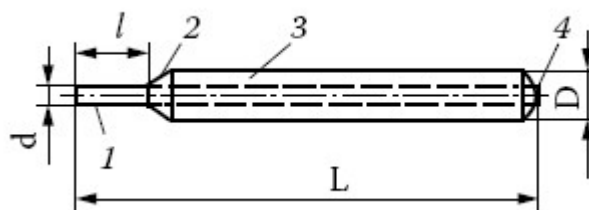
Сварочный плавящийся электрод с покрытием:
